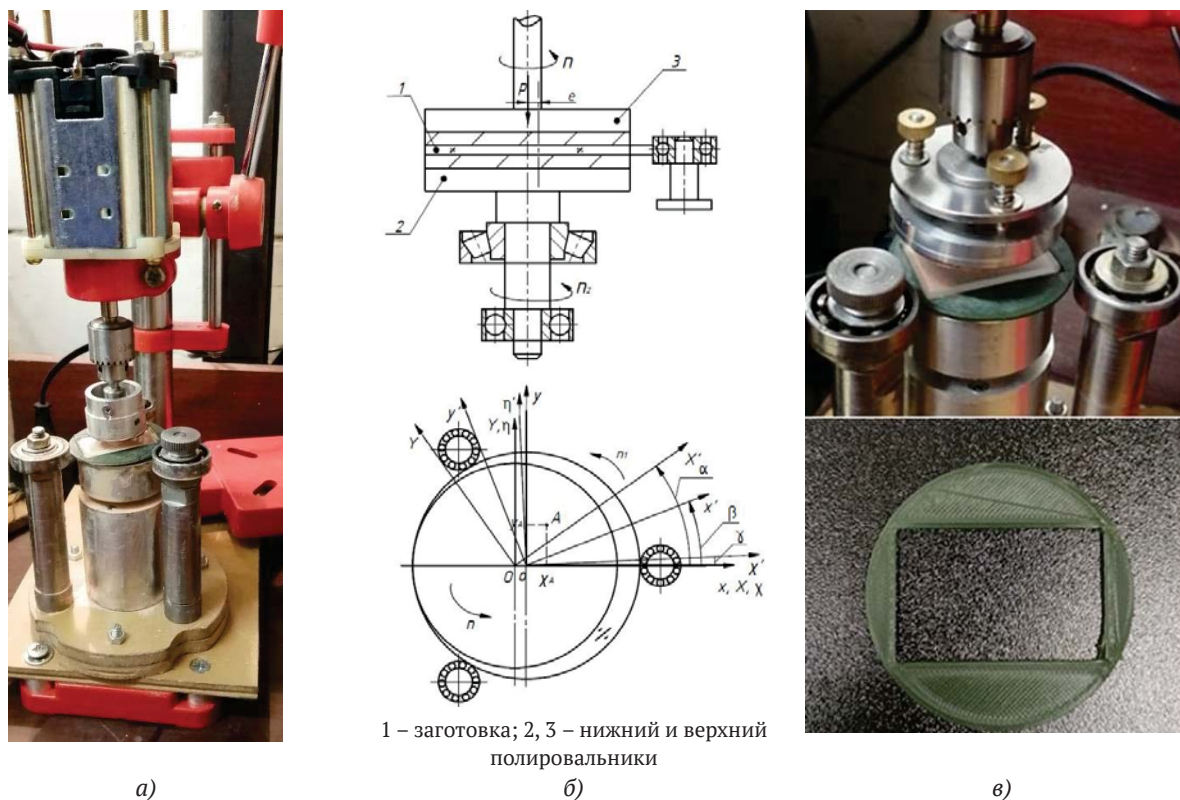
Предлагаемый станок новой конструкции для индивидуального двухстороннего полирования круглых и имеющих сложную форму оптических деталей: а) внешний вид; б) расчётная схема формообразования оптических поверхностей; в) применяемая конструкция сепаратора
